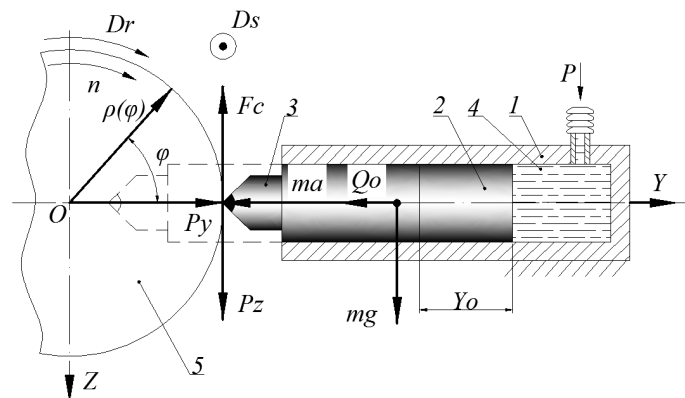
Схема вигладжування зовнішніх функціональних поверхонь кілець роликових підшипників: 1 – корпус інструменту; 2 – поршень; 3 – індентор; 4 – робоча рідина; 5 – заготовка
